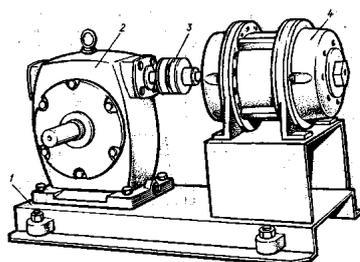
Установка привода на сварной раме из листовой стали:
